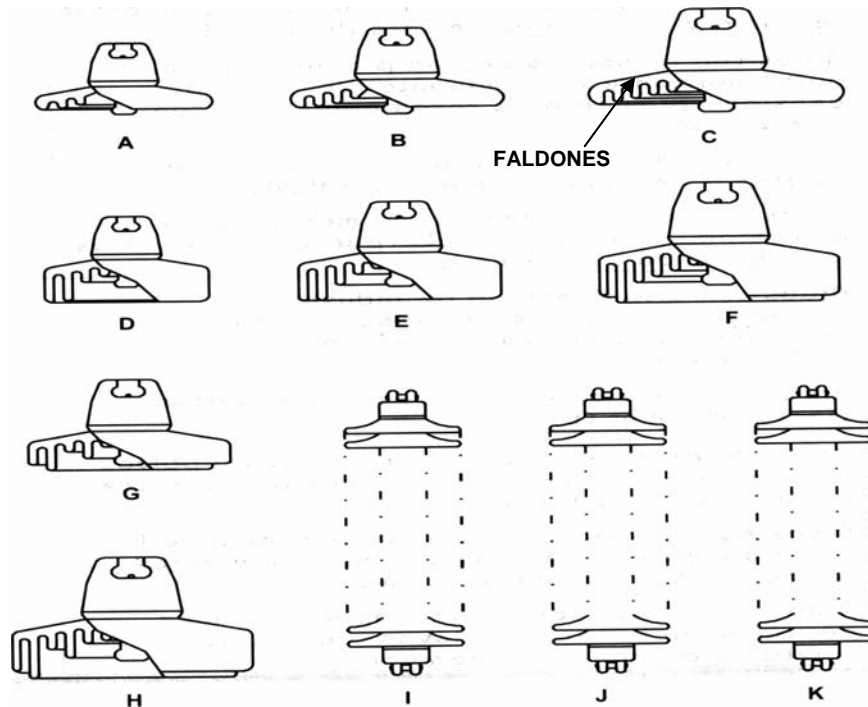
PERFIL DE AISLADORES TIPO SUSPENSIÓN
